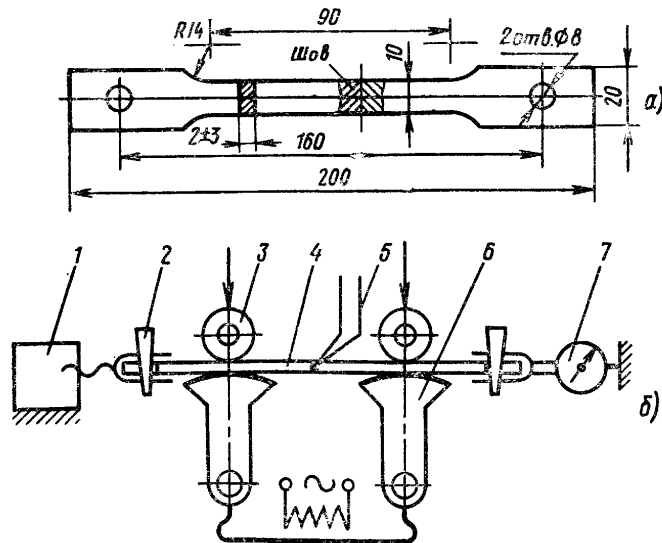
Эскиз образца (а) и схема машины (б) для оценки прочности и пластичности металла в условиях сварки: 1 — многоступенчатый механизм растяжения; 2 — клиновидный штифт-компенсатор; 3 — прижим; 4 — образец; 5 — термopapa; 6 — токоподводящий сектор; 7 — динамометр
